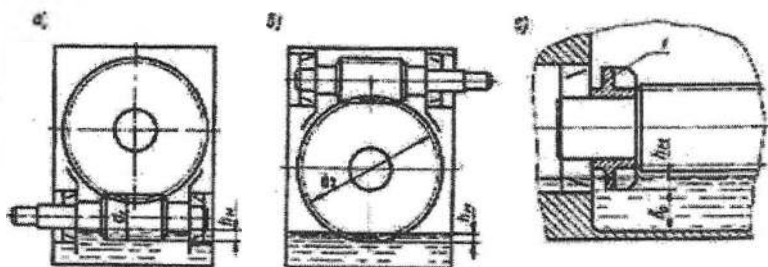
Глубина погружения в масло деталей червячного редуктора.
